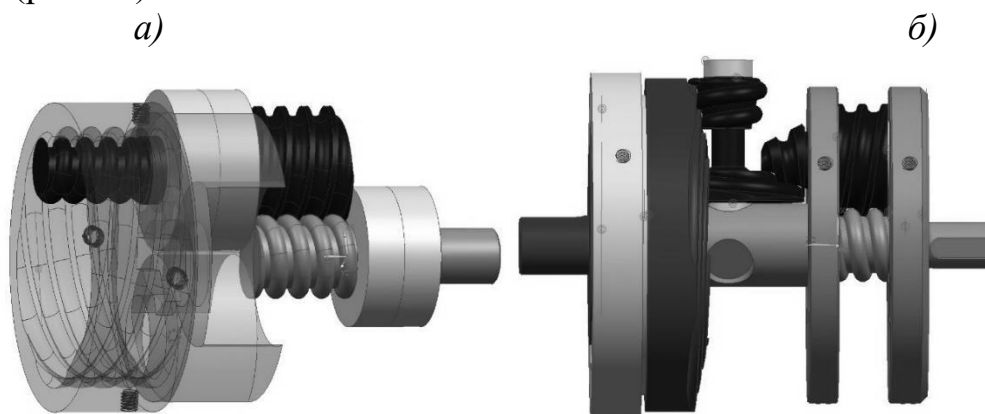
3D модели двух- и трехступенчатой передачи с резьбовыми роликами
